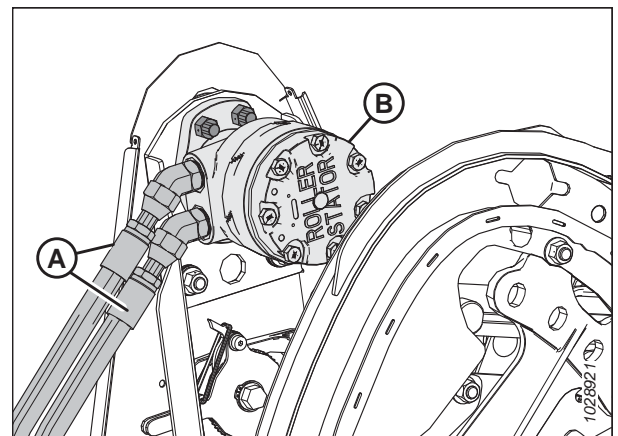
Haspelmotor und Hydraulikschläuche
